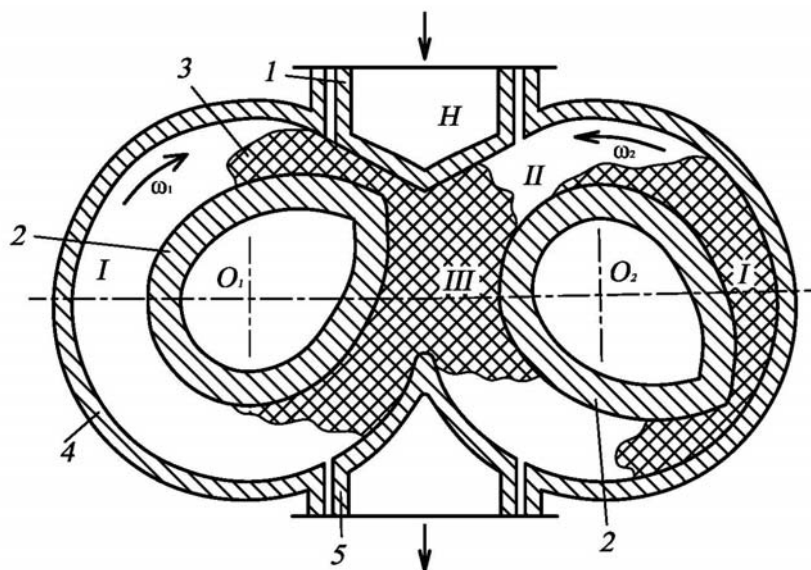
Схема двороторного змішувача закритого типу: 1 і 5 — верхній і нижній затвори; 2 — ротори; 3 — композиція; 4 — камера змішувача; I, II, III — зони змішування
